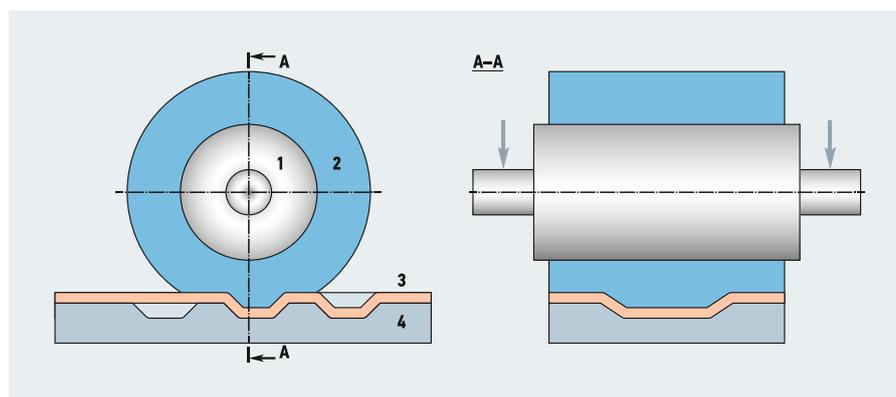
Схема формовки плоской детали (1 — жёсткий валок; 2 — эластичное покрытие; 3 — деталь; 4 — матрица)
